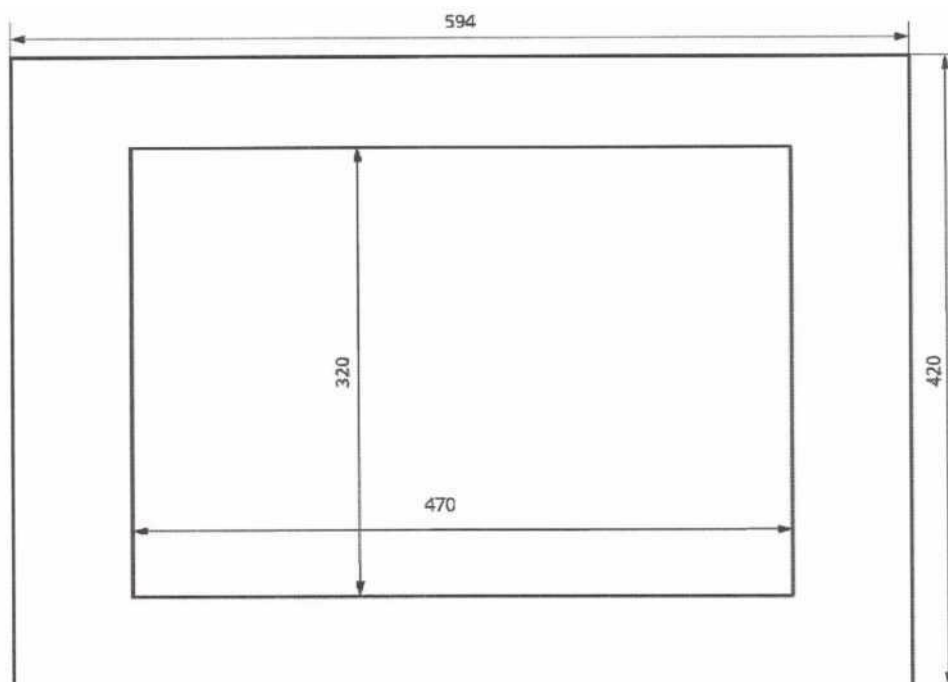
Схема розкладки заготовки для палітурки подарункового фотоальбому
